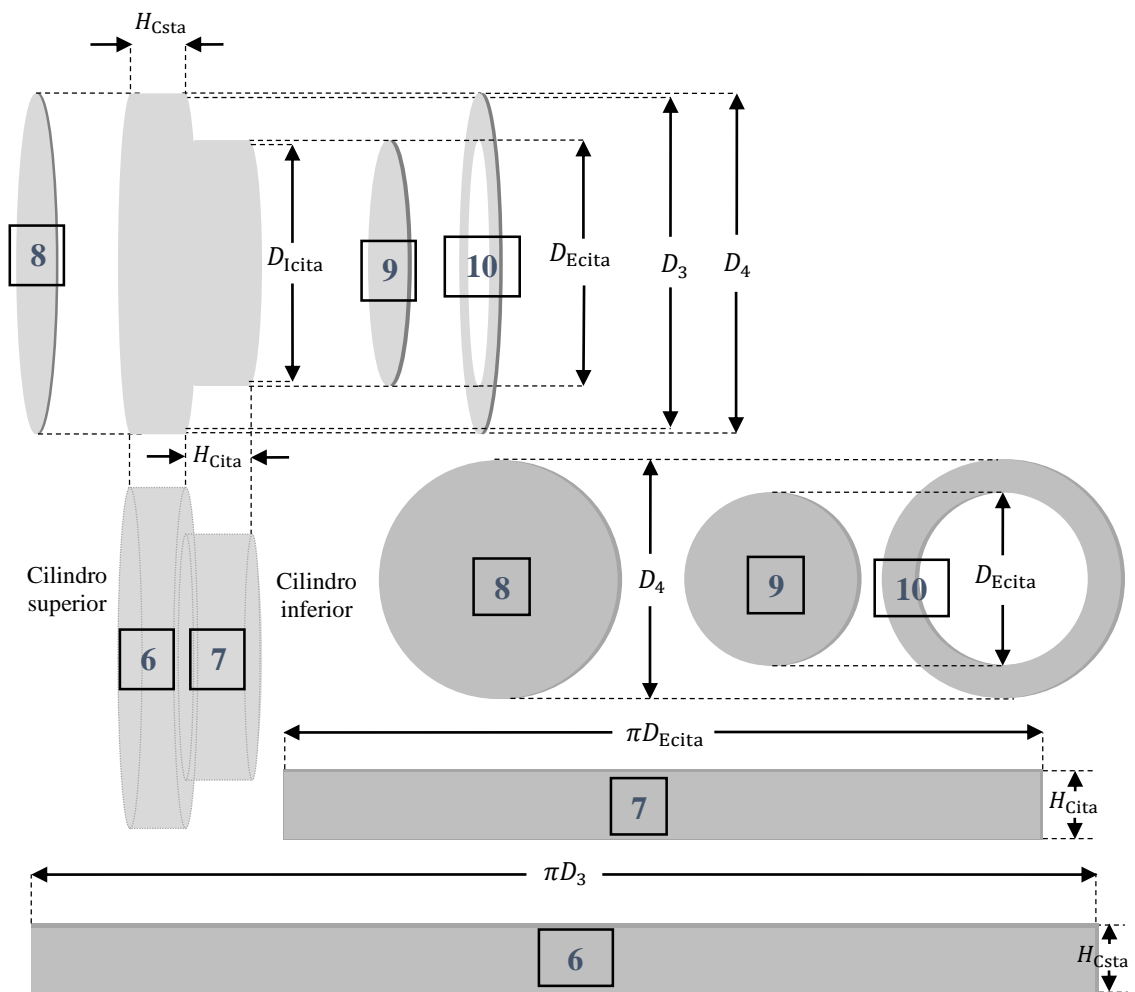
Fijación del aro entre los cilindros interior y exterior.
